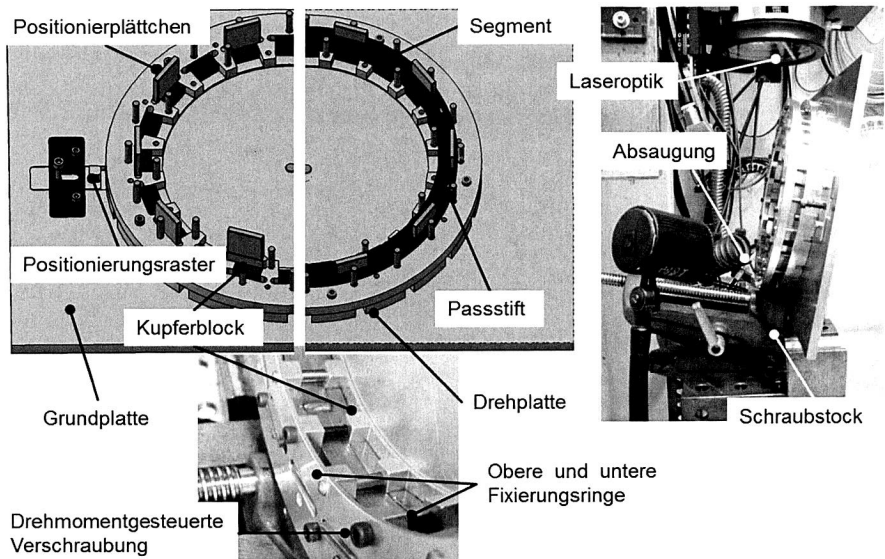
Vorrichtung zum Verbindungsschweißen von segmentierten Rotoren.
